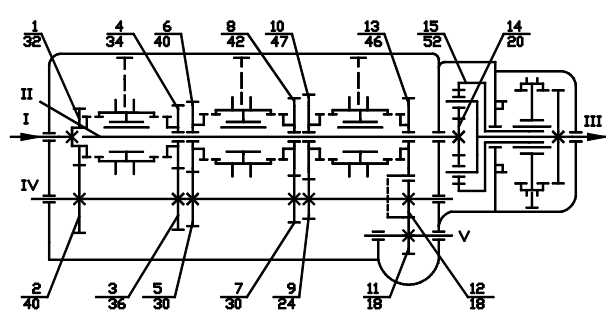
Коробка передач 9-ступенчатая с задним планетарным редуктором
